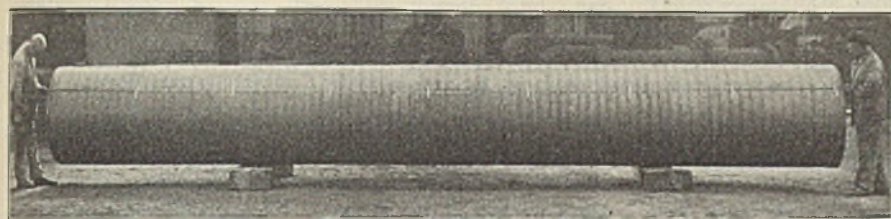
Ausgewalztes Rohr vor dem Glättstich. (Nahtloses Rohr aus Cu-Ni-Stahl TH 62, gewalzt nach DRP. 414 790. Gesamtlänge 8100 mm, Wandstärke 69 mm, lichter Durchmesser 900 mm.)
